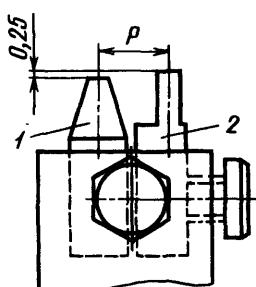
Блок из двух резцов для нарезания трапецидальной резьбы:
